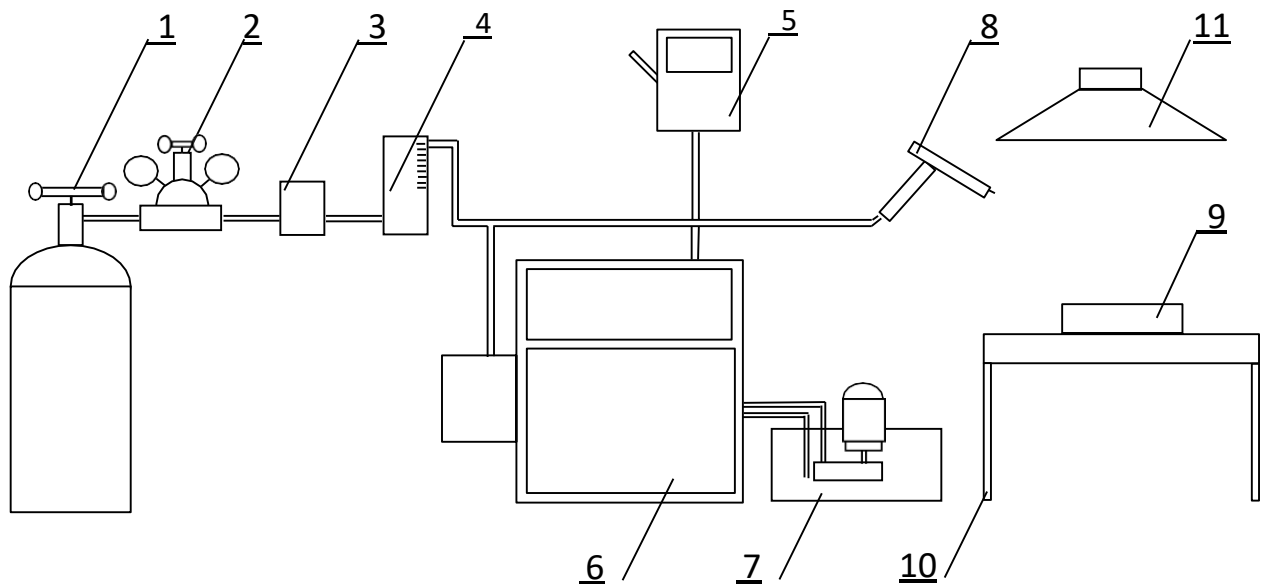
Схема рабочего поста для аргонодуговой сварки
